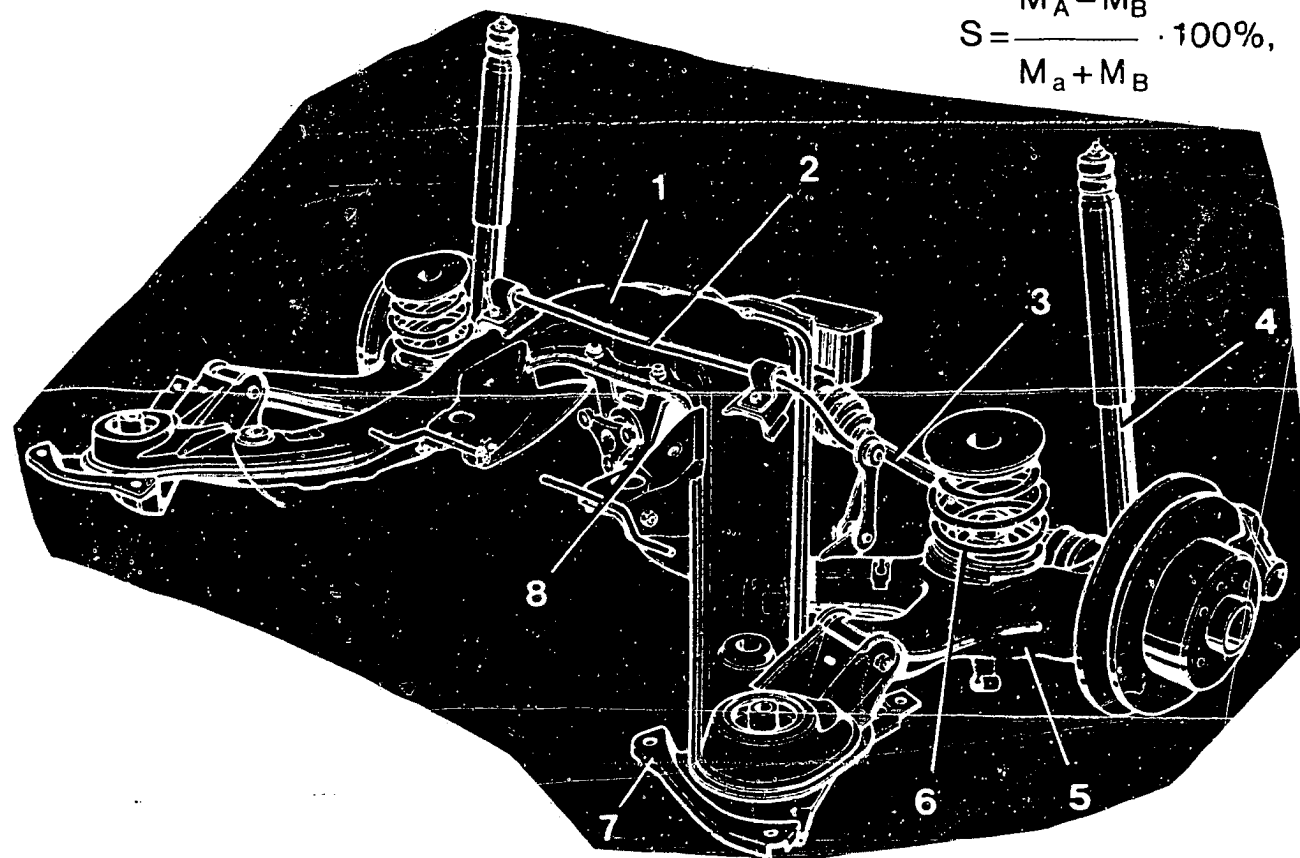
Hinterradaufhängung mit 1 Querträger – 2 Stabilisator – 3 Antriebswelle – 4 Stossdämpfer – 5 Schräglenker mit Achsschenkel – 6 Schraubenfeder – 7 Querträger-Befestigungsstreben – 8 Ausgleichsgetriebe.
